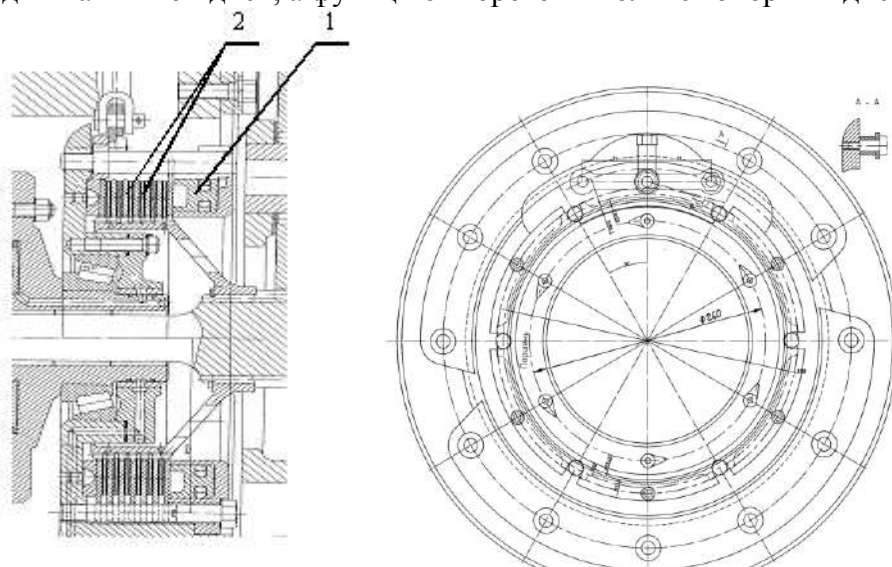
Предлагаемая конструкция тормозного механизма
